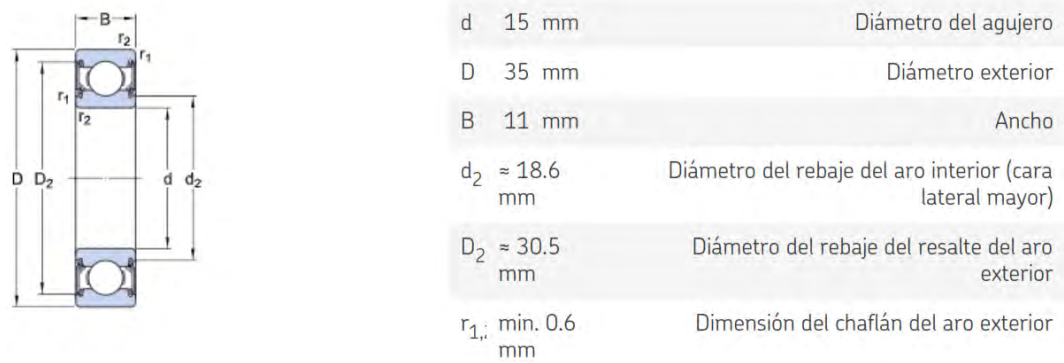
Dimensiones de rodamiento rígido de bolas 6202-2RSH
